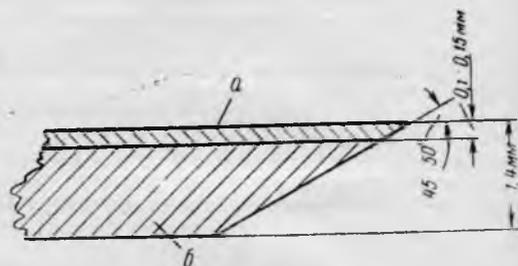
Сечение звена из двухслойной стали по режущему зубу:
